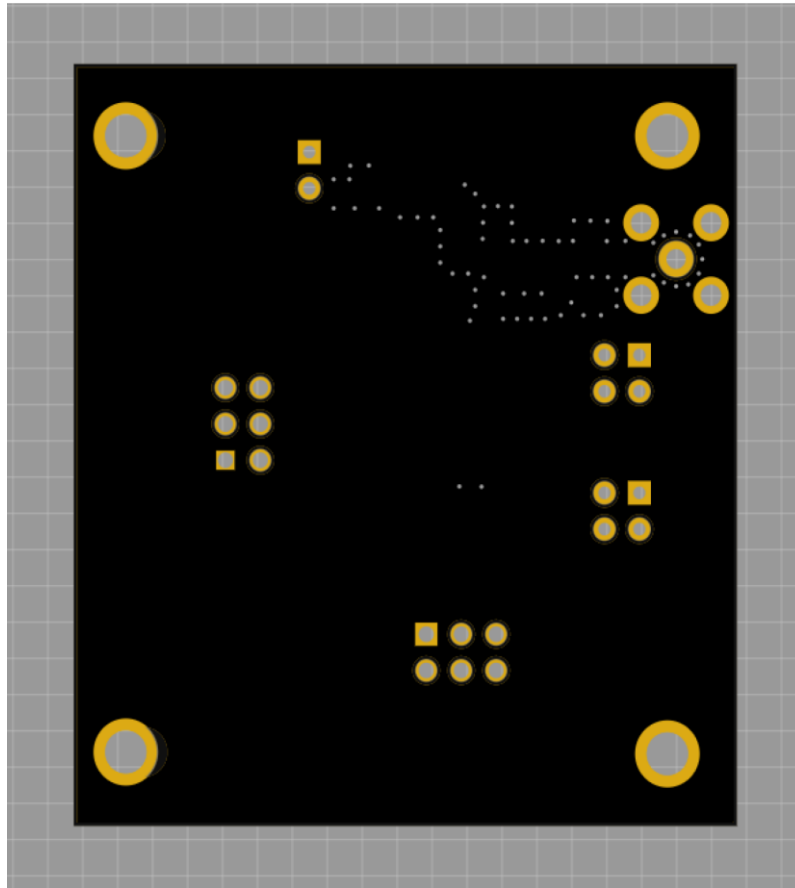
Фото-вид зворотної сторони друкованої плати без елементів
